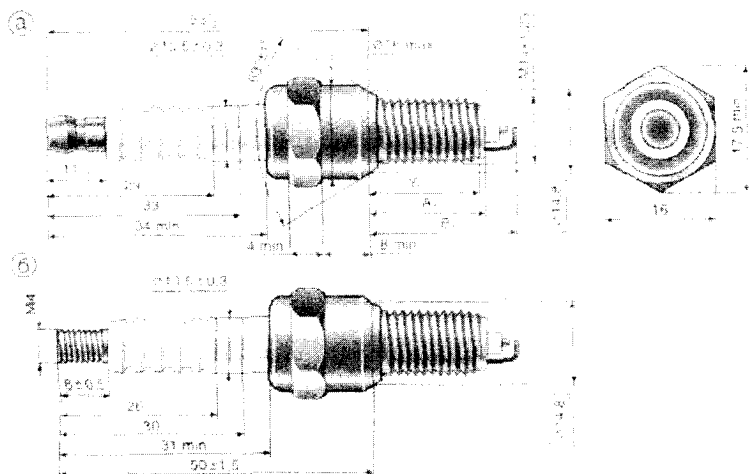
Габаритні й приєднувальні розміри свічок М14×1,25 з конічною опорною поверхнею: а – зі штировою контактною головкою; б – з різьбовою контактною головкою
